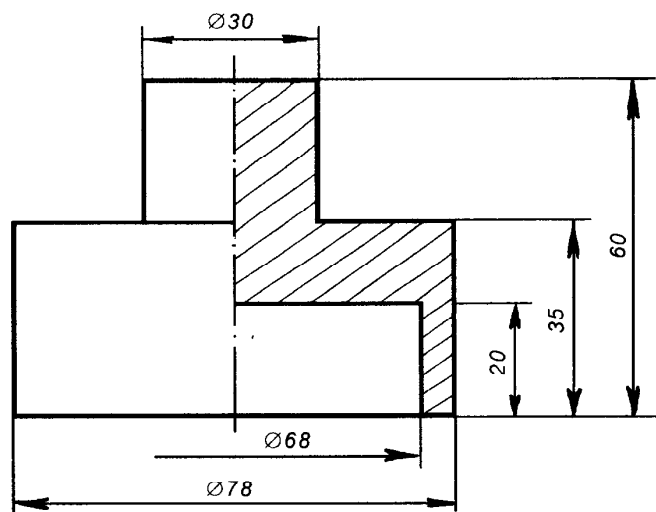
Оправка для запрессовки манжеты в крышку распределительных шестерен
